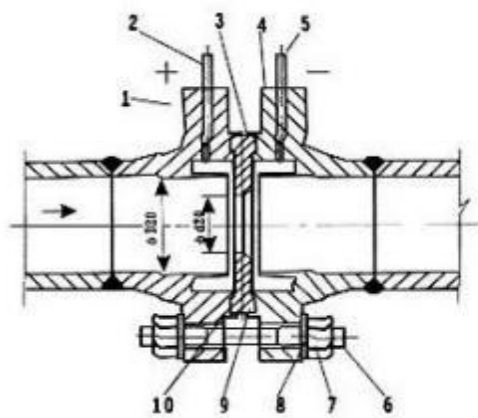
Стандартная диафрагменная конструкция для отбора давления кольцевой камеры (DN≤400, PN≤10МПа) Рис. 3.5 Стандартная диафрагменная конструкция для отбора давления кольцевой камеры (DN≤400, PN≤32МПа)
